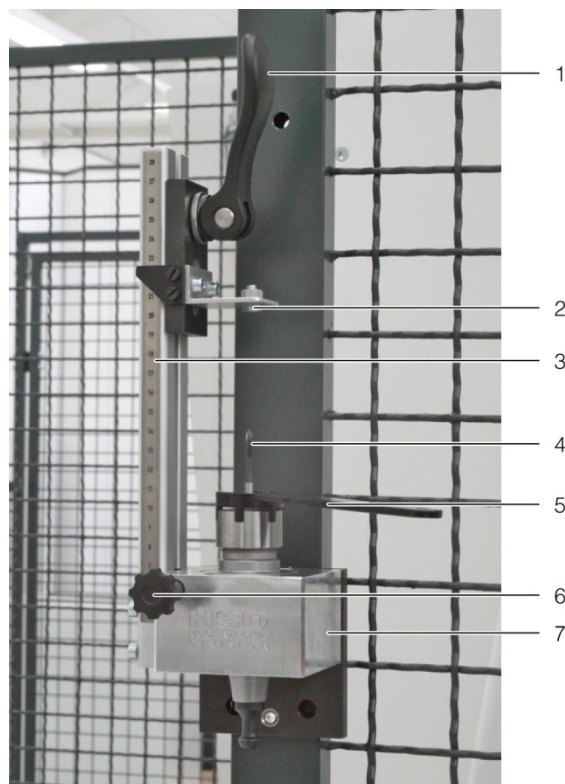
Werkzeugmontagehilfe (Zubehör)
